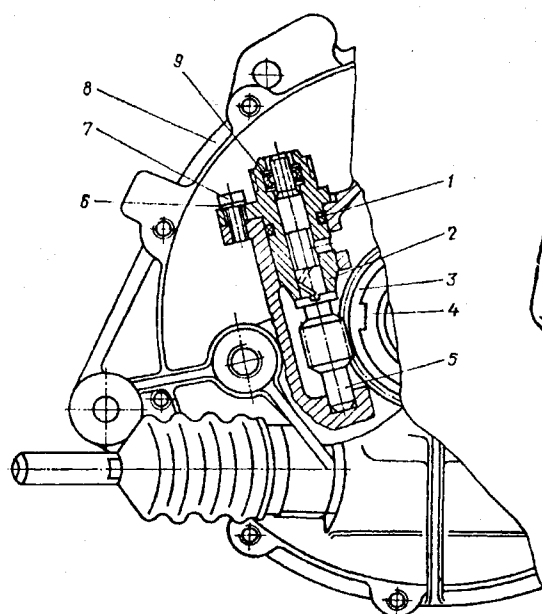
привод спидометра: 1 – уплотнительное кольцо; 2 – корпус привода спидометра; 3 – ведущая шестерня; 4 – коробка дифференциала; 5 – вал – шестерня ведомая привода спидометра; 6 – шайба; 7 – болт; 8 – картер сцепления
